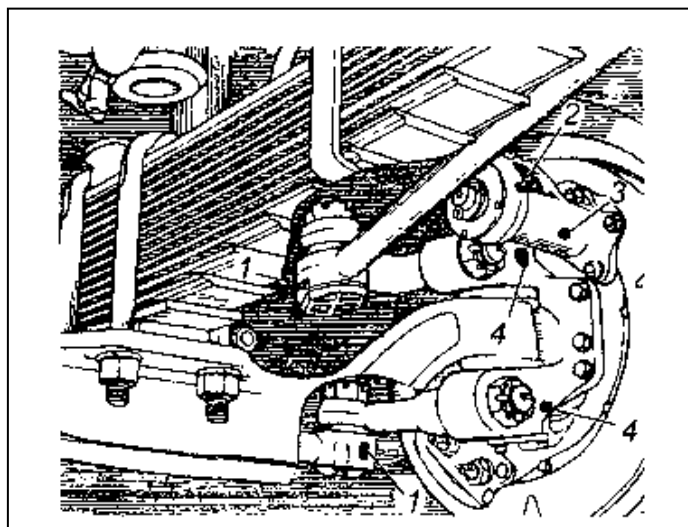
Расположение на автомобиле пресс-масленок для смазывания: 1 — шарниров рулевых тяг; 2 — регулировочного тормозного рычага; 3 — разжимного кулака; 4 — втулок шкворней
